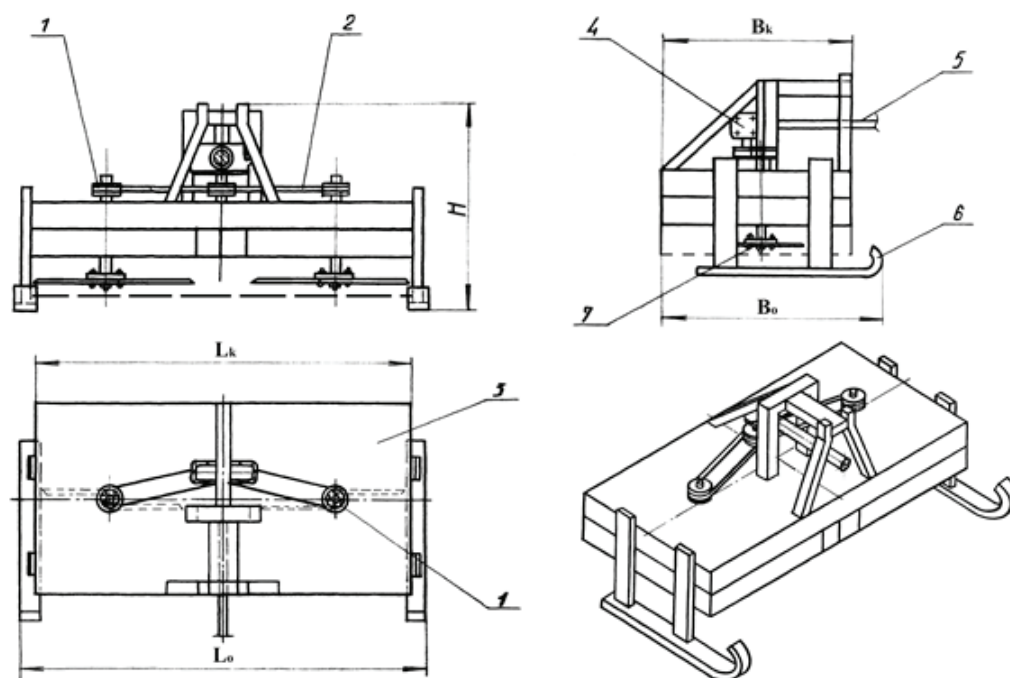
Приспособление для измельчения стеблей хлопчатника: 1 – шкив; 2 – ремень; 3 – корпус; 4 – редуктор; 5 – карданный вал; 6 – ползья; 7 – ножи; Н – высота машины; L_k – длина корпуса; L_o – общая длина машины; B_k – ширина корпуса; B_o – общая ширина машины
